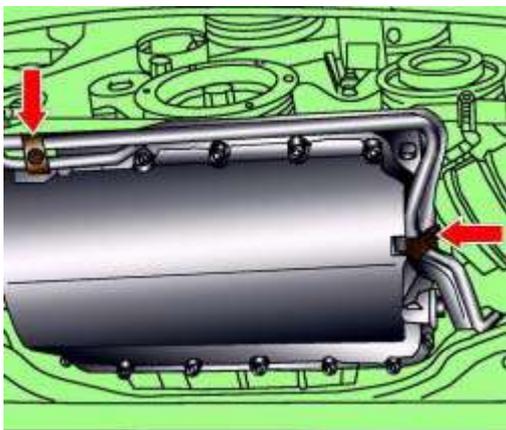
Расположение болтов крепления кронштейнов, поддерживающих трубопроводы, к автоматической коробке передач
